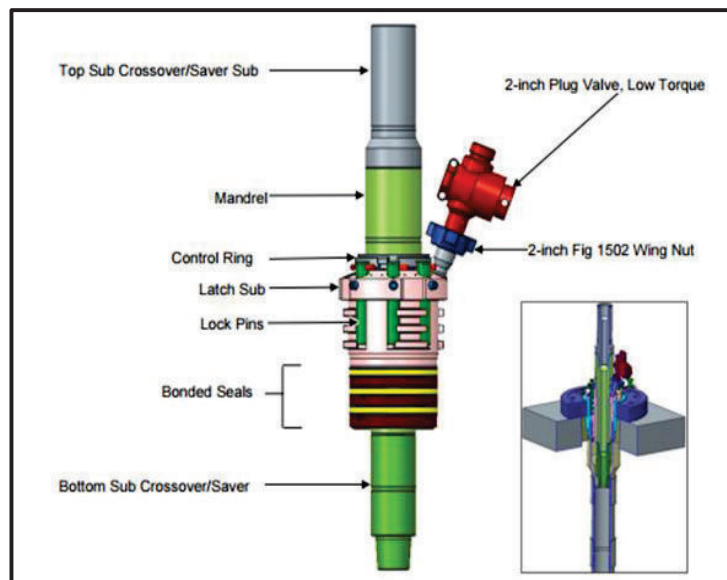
Ensamblaje de Cerrojo y Cierre (Izquierda), Herramienta de Circulación del Casing (Derecha)
